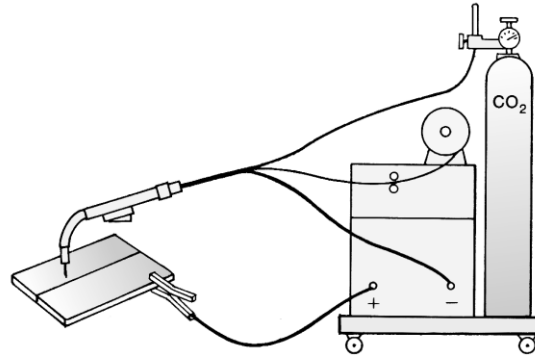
Esquema básico de un equipo para soldadura MIG.
